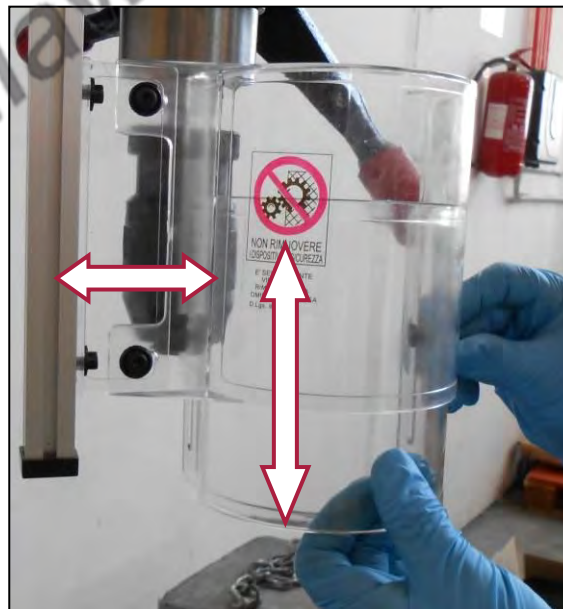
Scorrimenti del riparo in senso verticale e longitudinale
